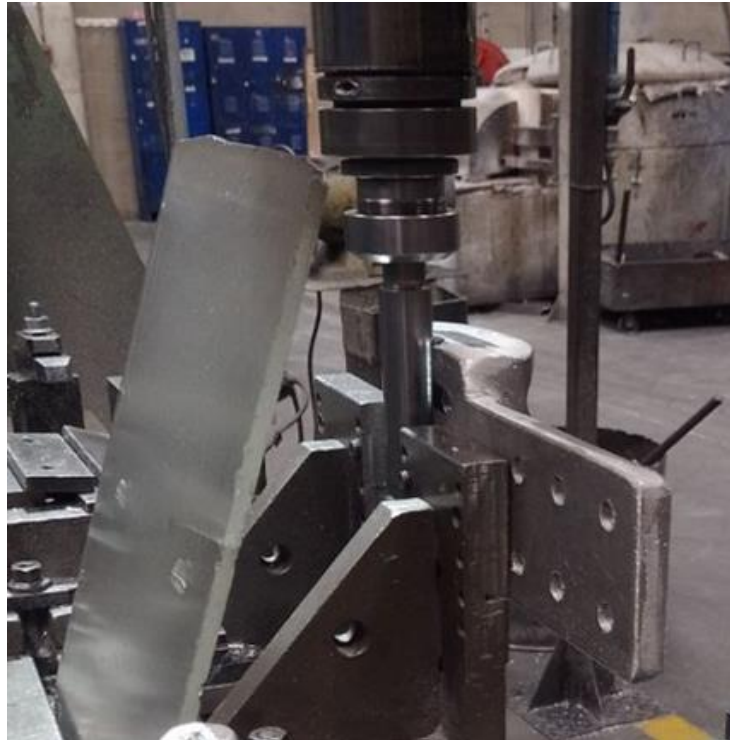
Montaje para mecanizado de radio con buril y dispositivo de sujeción.
